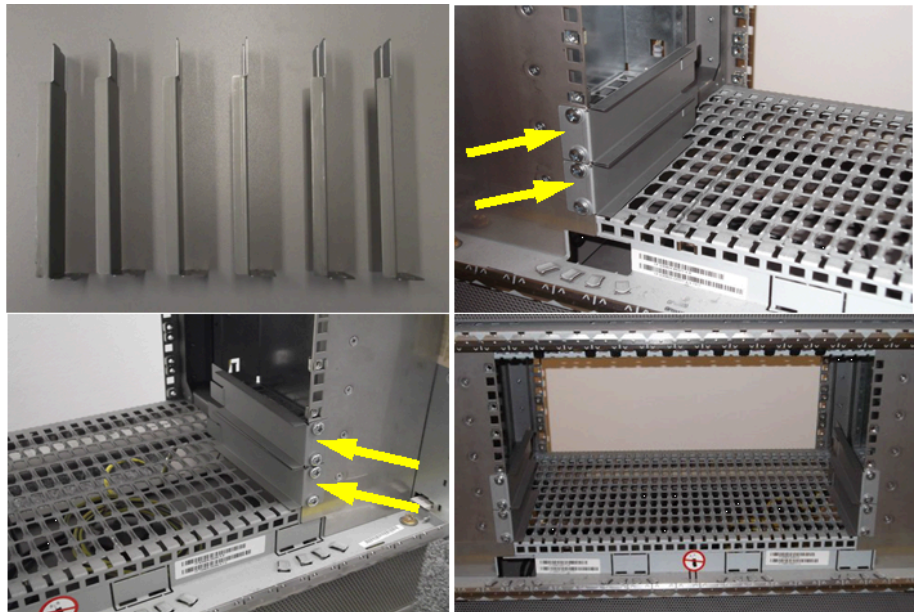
Montaggio della piastra di ventilazione (lato anteriore)
